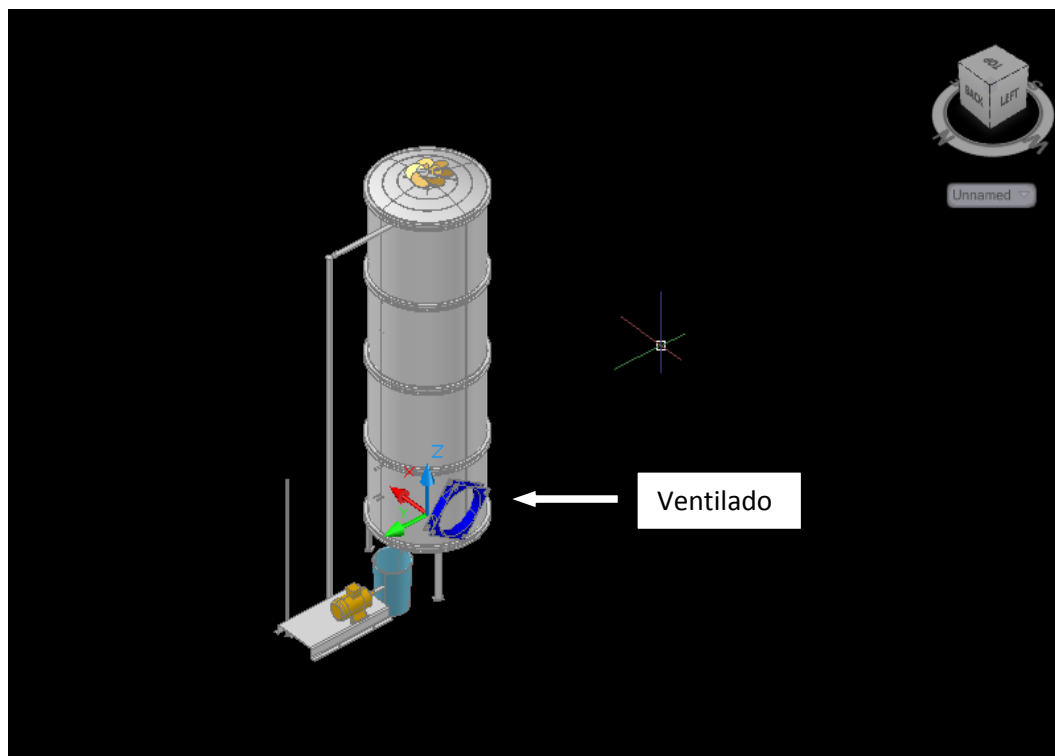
ventilador en el cuerpo de la columna de absorción.
